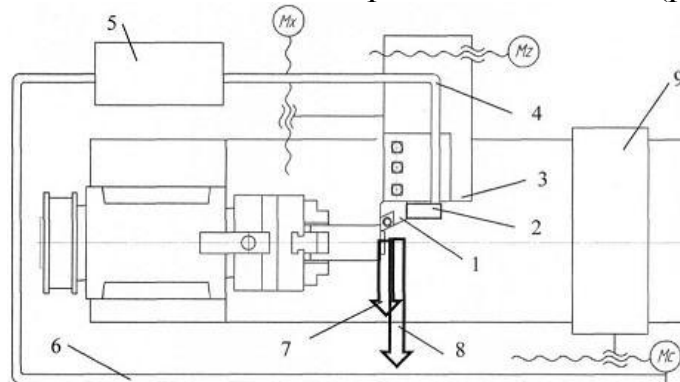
Спосіб динамічного керування коливаннями супорта верстата. 1 – різець; 2 – датчик віброприскорення; 3 – супорт; 4 – канал зв'язку датчика з блоком керування; 5 – блок керування; 6 – канал зв'язку привода додаткової маси; 7, 8 – вектори коливання інструменту; 9 – додаткова маса
